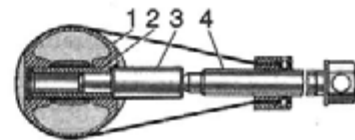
Выпрессовка поршневого пальца из поршня съемником:
